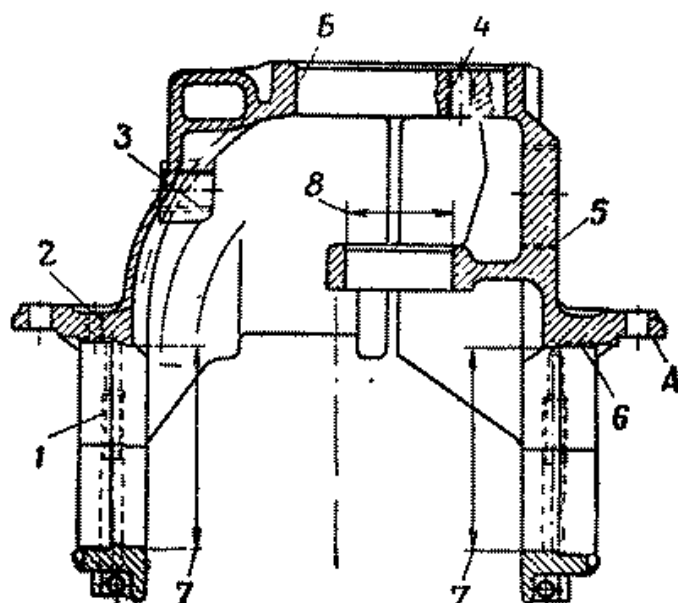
Картер редуктора моста с крышками подшипников дифференциала в сборе
